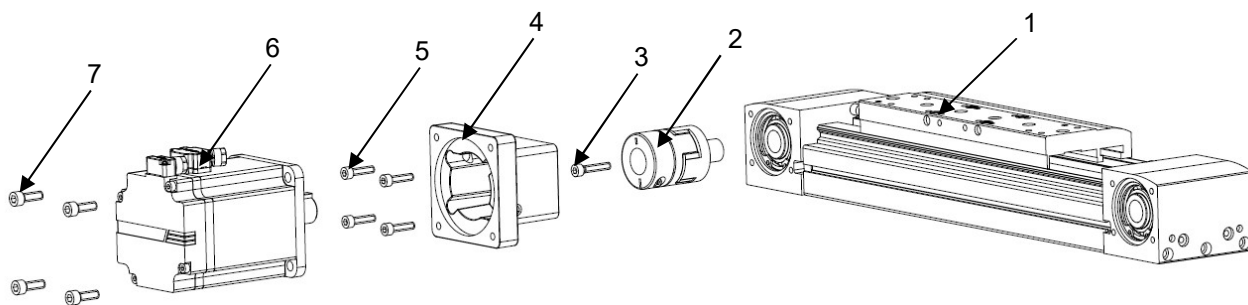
Установка двигателя с помощью монтажного комплекта модели AM-EGT
